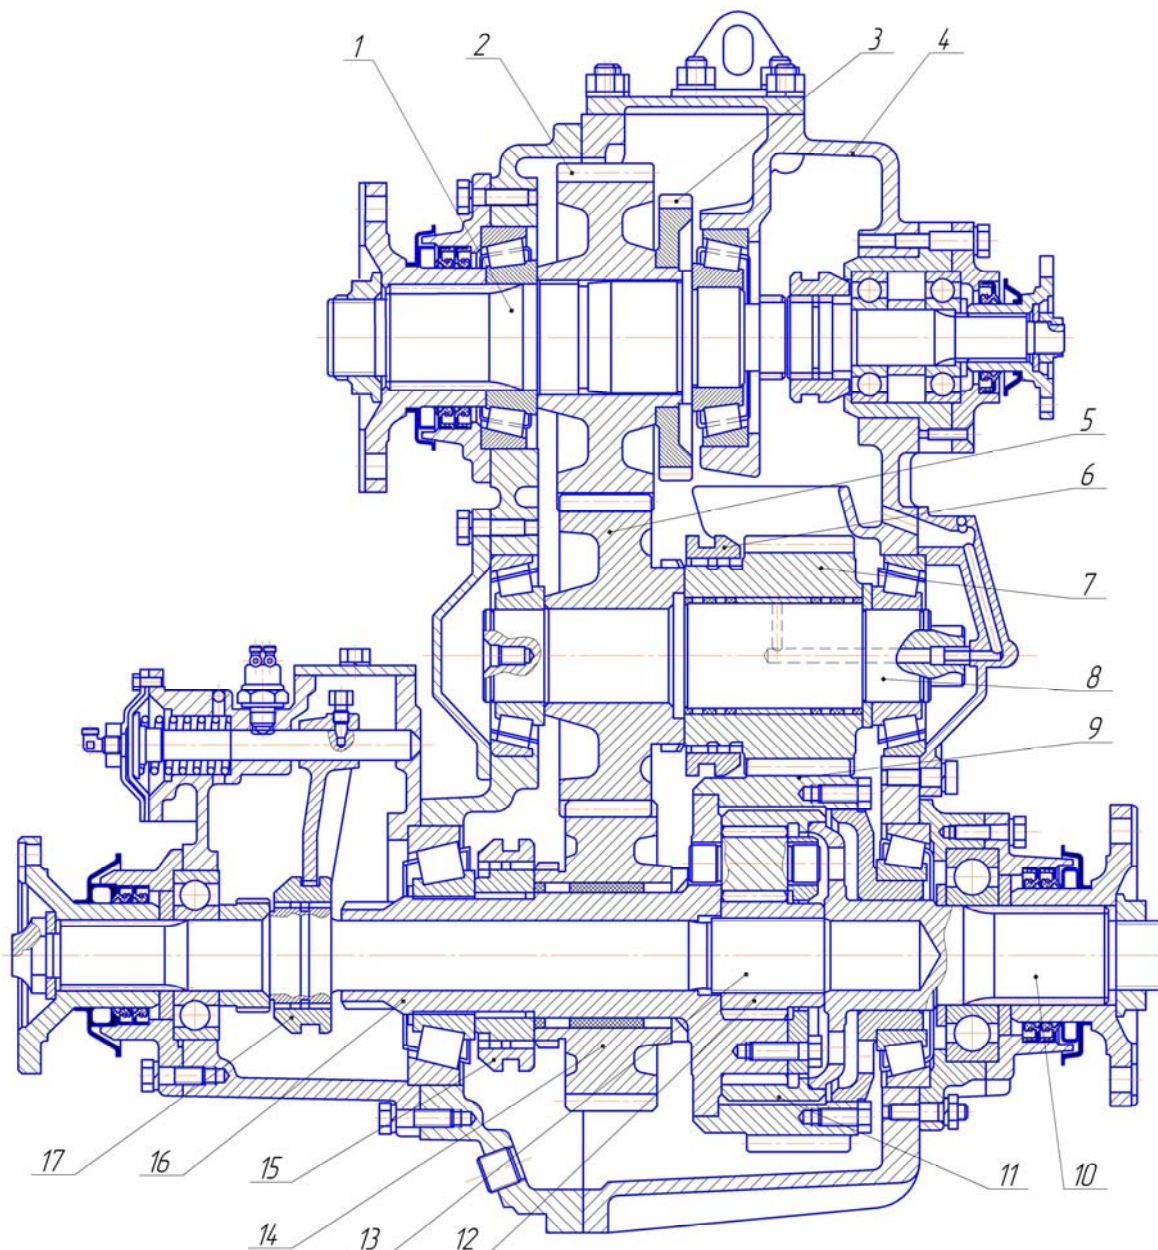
Раздаточная коробка автомобиля КамАЗ-4310
